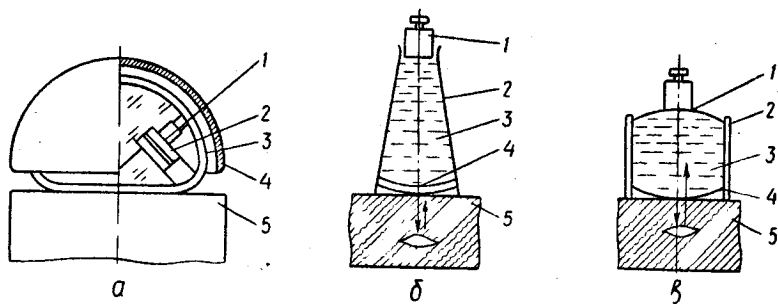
Схема шукачів для контролю грубої поверхні:
